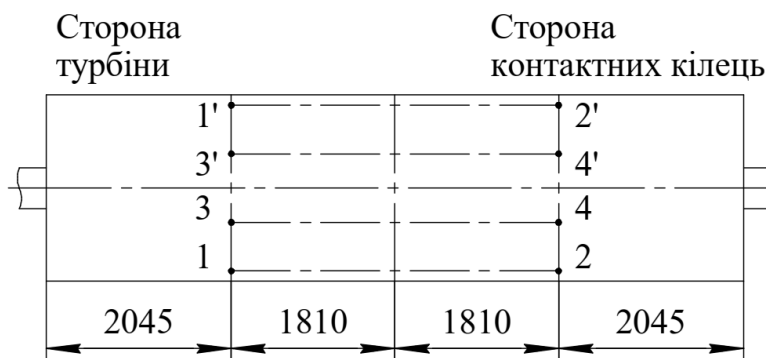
Розташування точок вимірювання на корпусі статора турбогенератора (вид зверху)
